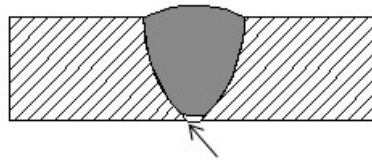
Неповний дефект зварювального проникнення
